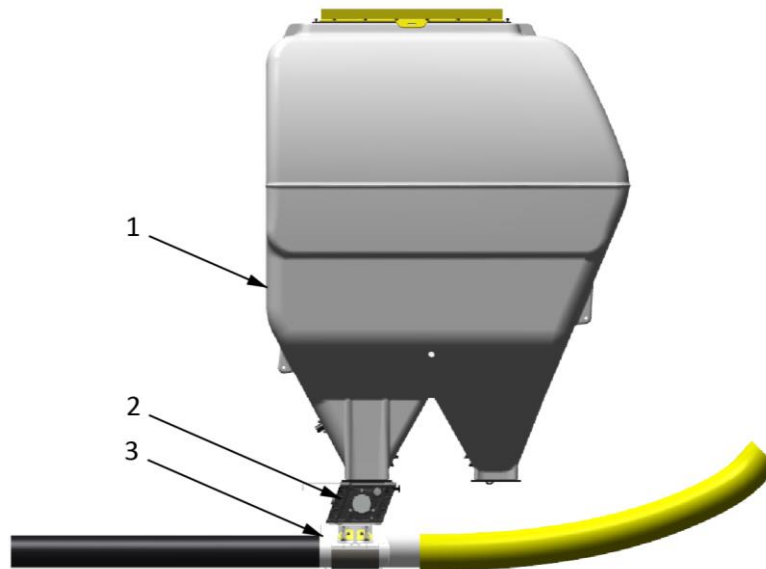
Bludiště pro zbrzdění proudu vzduchu
